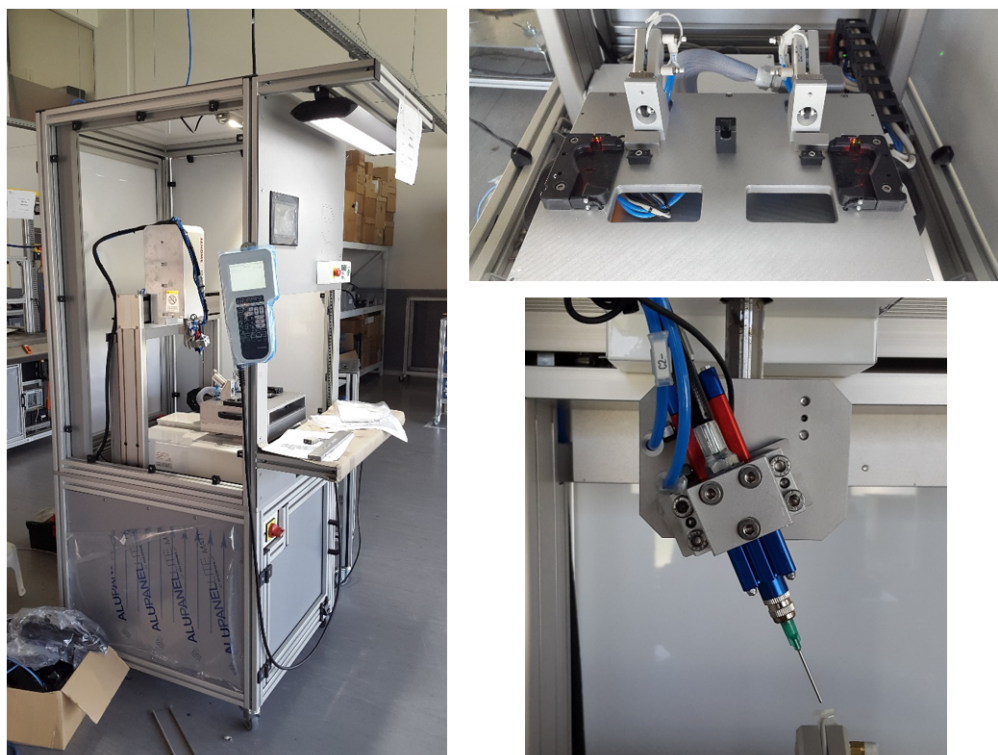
Equipamento durante montagem com detalhe do sistema de fixação e ferramenta de deposição.
